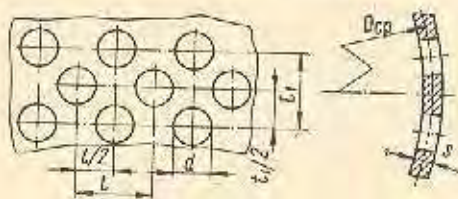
Шахматное расположение отверстий в цилиндрической обечайке
